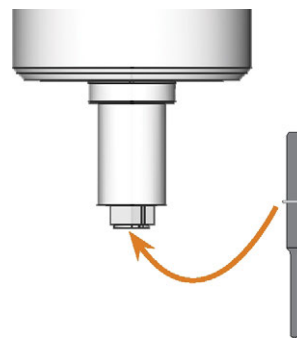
DAS WERKZEUG IN DIE SPANNZANGE EINFÜHREN
